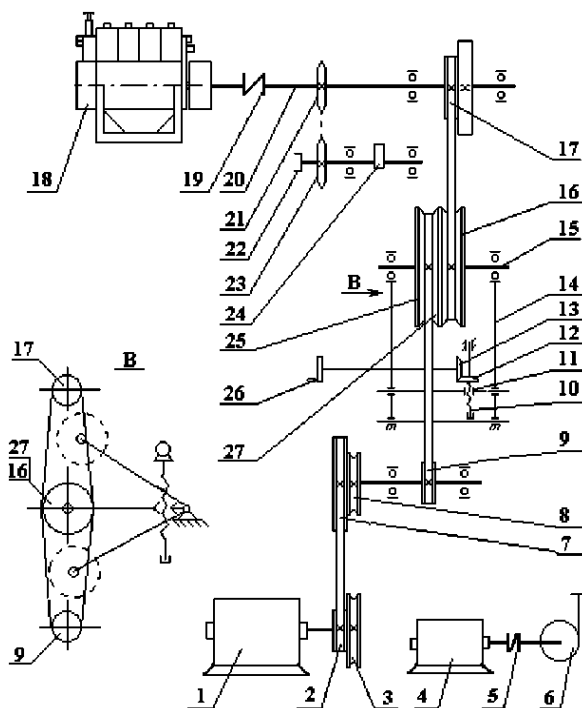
Кинематическая схема стенда КИ-22205:
